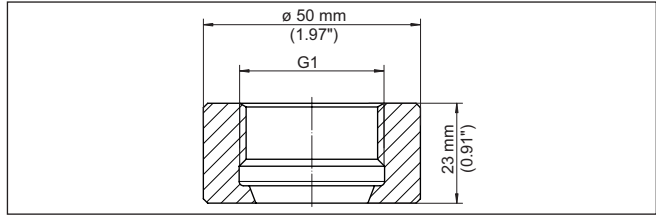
Dimensiones racor para soldar G1 (ISO 228-1) - Junta cónica
